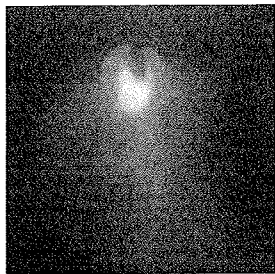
In-Prozess-Aufnahme beim Schweißen einer Bördelnaht mit einem Spalt von 0,2 mm zwischen den Blechen.
